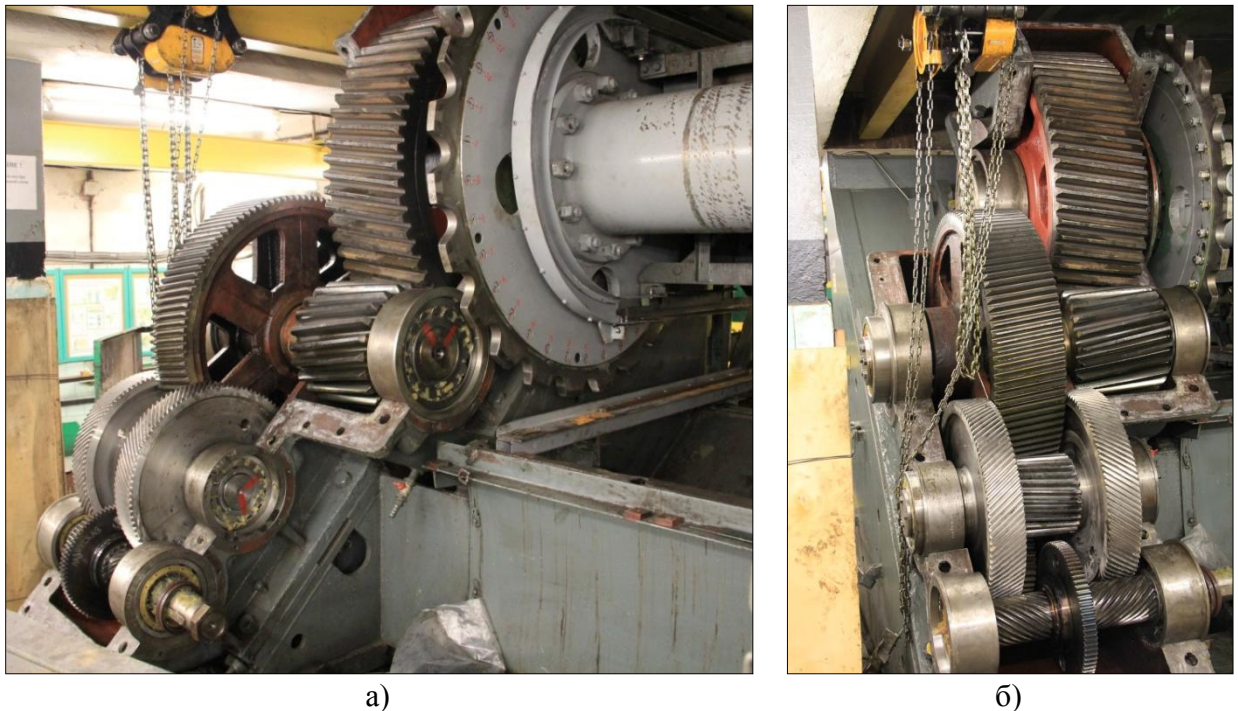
Установленные валы главного привода эскалатора ЭТ-2
